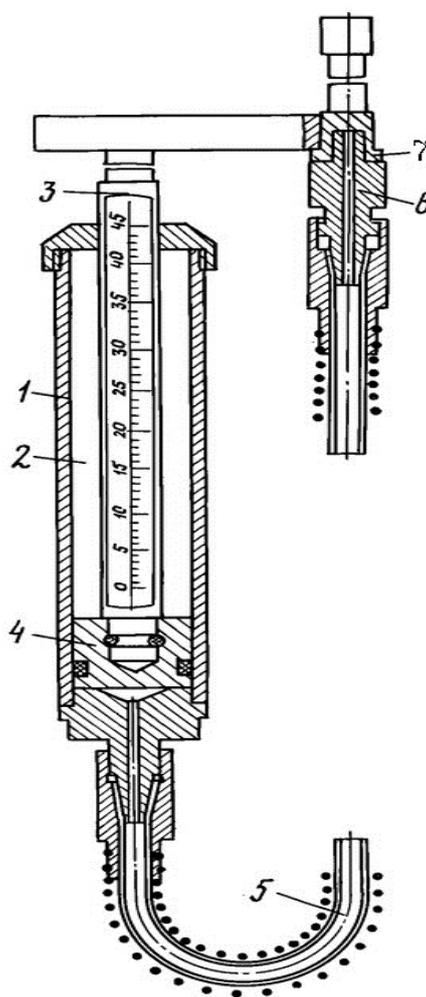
патент РФ № 2218517 общий вид шприца;
